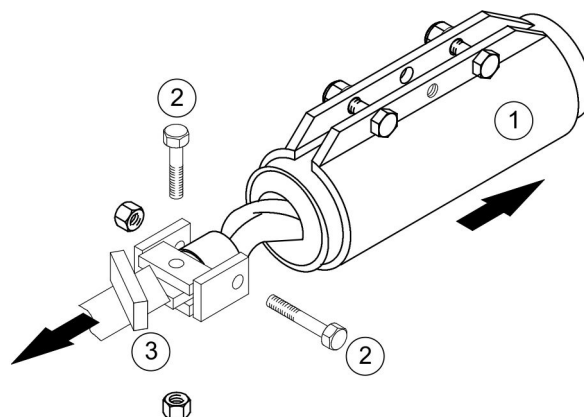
Extraer la bomba helicoidal (diferentes versiones posibles)
